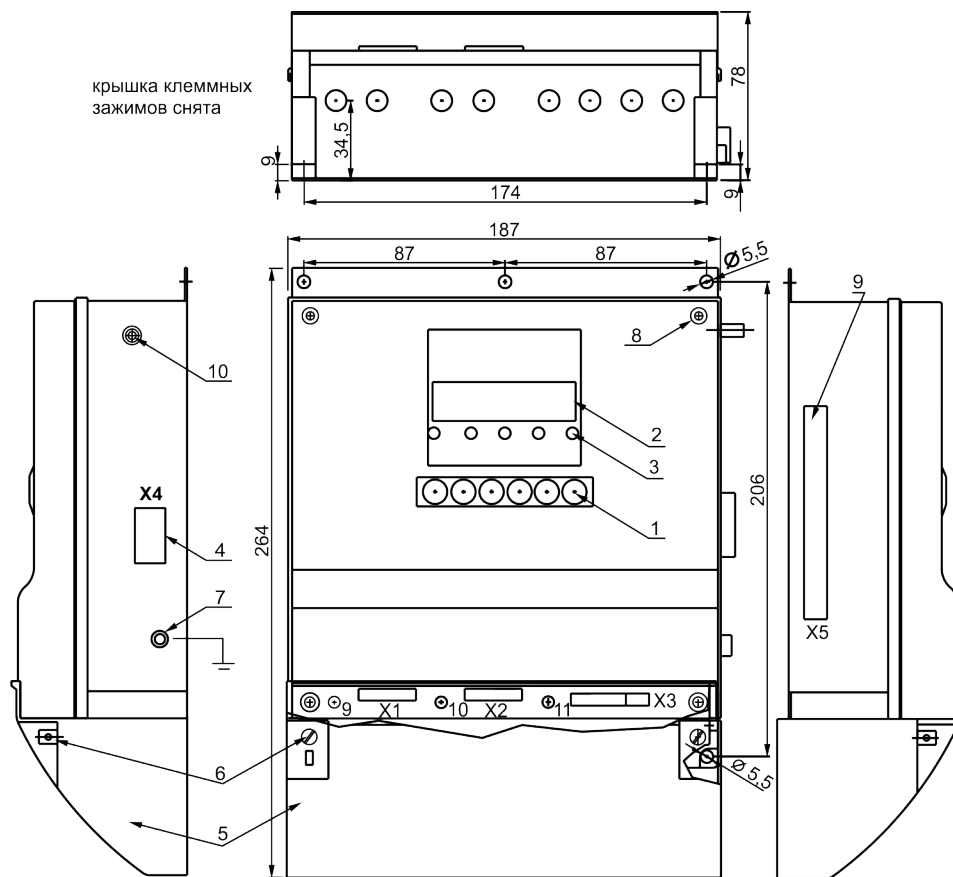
БИМ 4XXX в металлопластиковом корпусе
